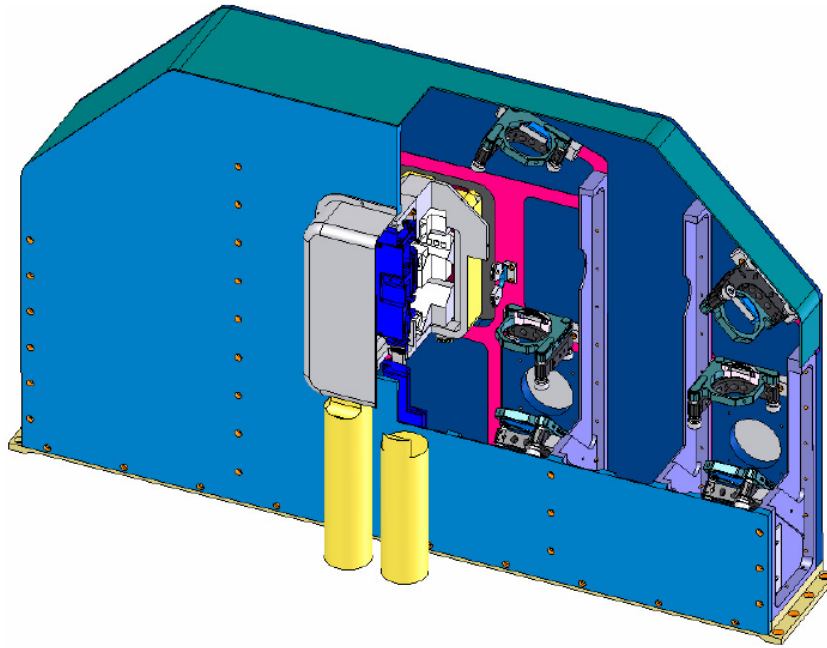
Estrutura da câmara de aquisição em corte parcial.
